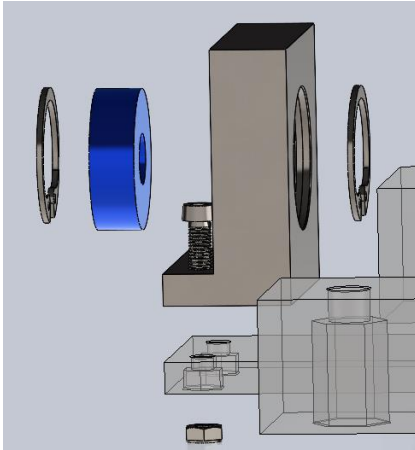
SUPORT DEL RODAMENT BASE 1 MECANITZAT AMB LA FRESADORA
